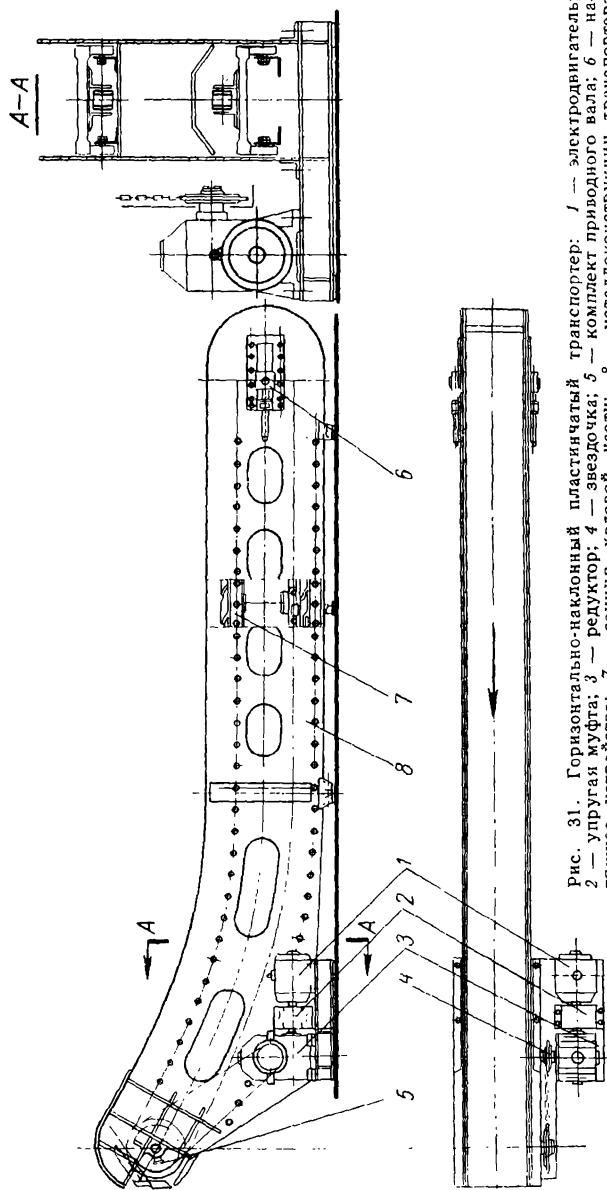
Горизонтально-наклонный пластинчатый транспортер: 1 — электродвигатель; 2 — упругая муфта; 3 — редуктор; 4 — звездочка; 5 — комплект приводного вала; 6 — на-тяжное устройство; 7 — секция ходовой части; 8 — металлоконструкция транспортера
